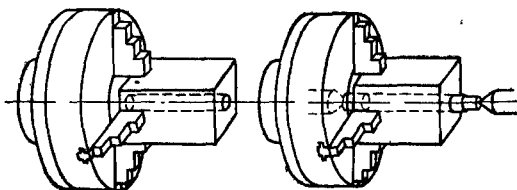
Выверка детали прямоугольной формы с помощью цилиндрической оправки.
